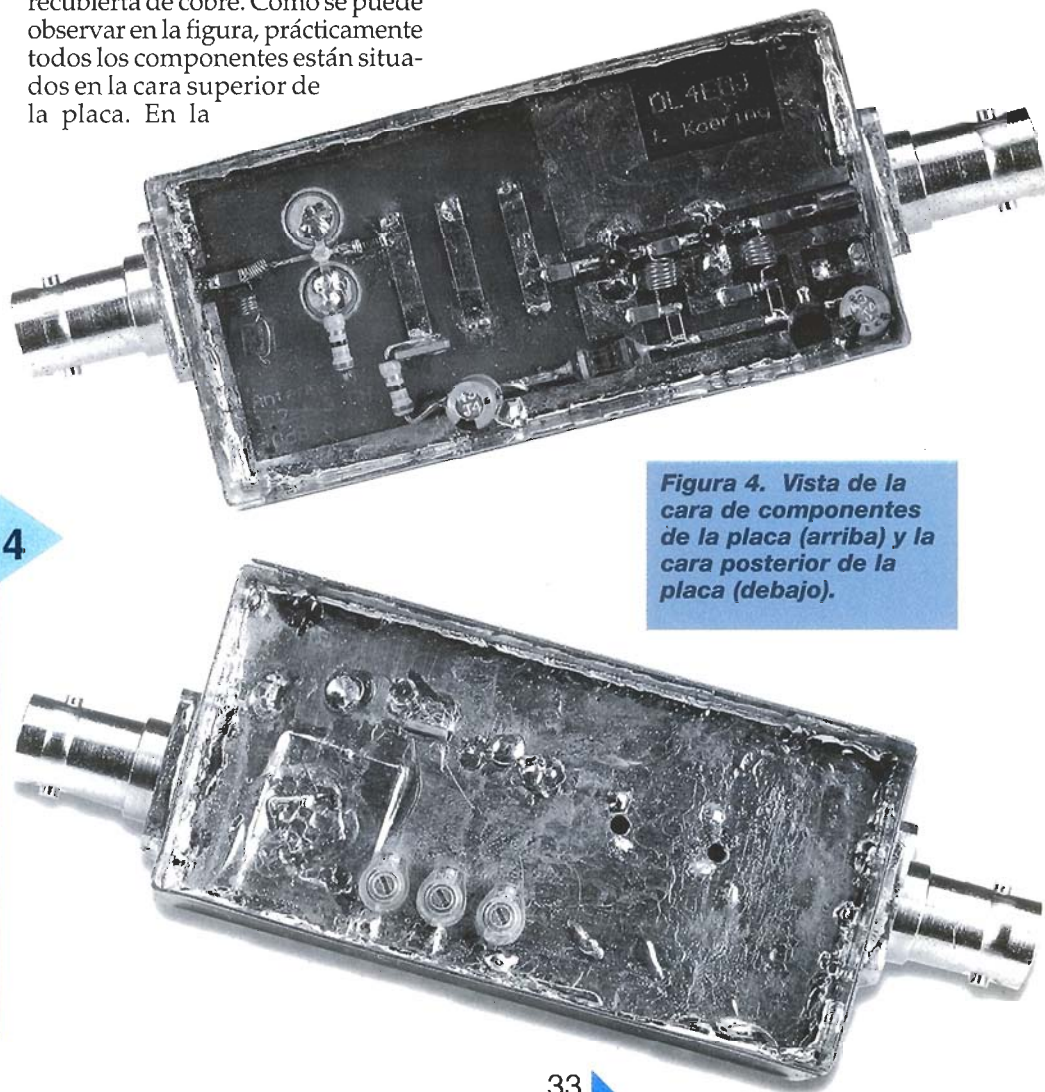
Vista de la cara de componentes de la placa (arriba) y la cara posterior de la placa (debajo).
